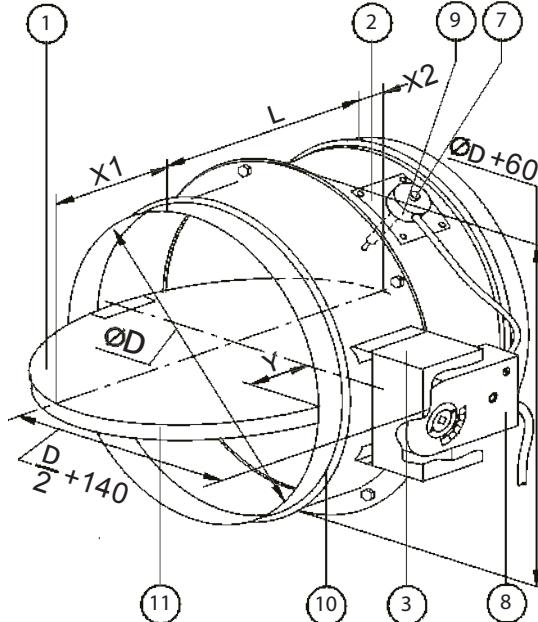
Конструкция и основные размеры клапанов [мм]:
